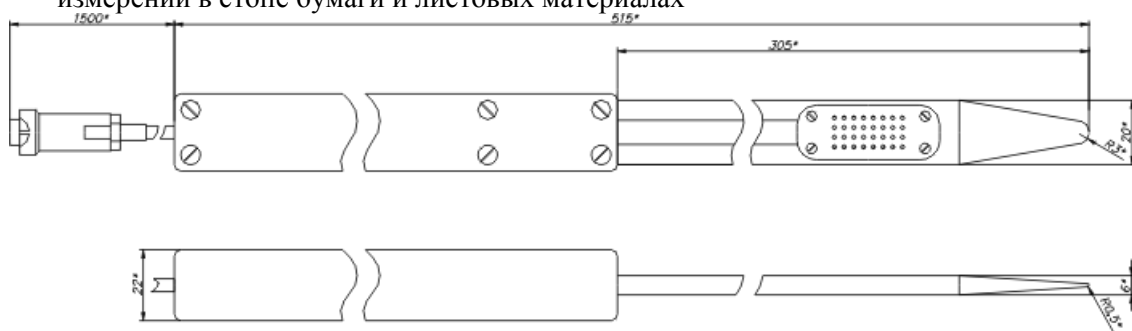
Измерительный преобразователь ИПВТ-03-11-ПВ
